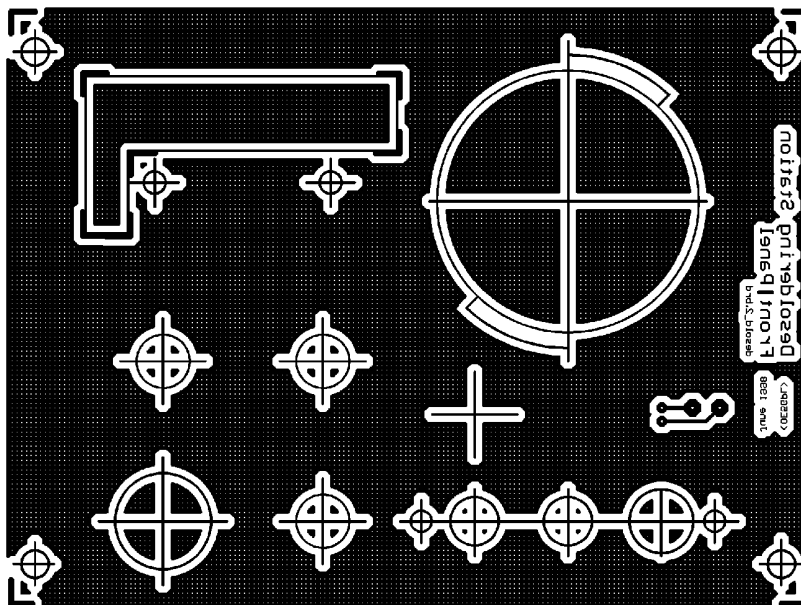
Geräteträger-Layout (nicht maßstabgetreu, Originalmaß 150*112 mm))
